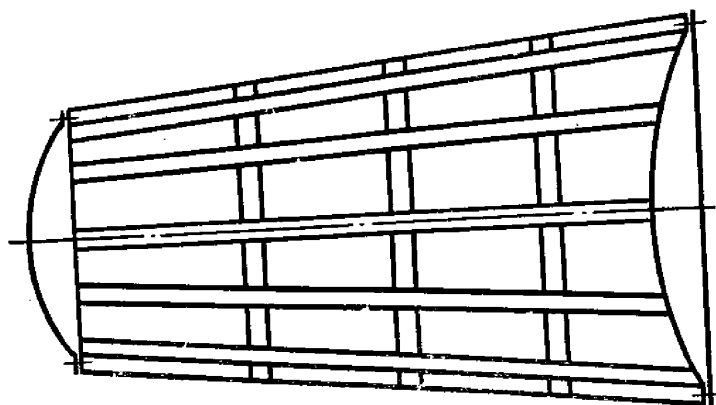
Конструктивная схема корпуса приборного отсека
